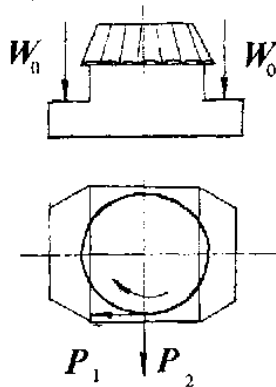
Затиск заготовки прихватами при фрезеруванні
